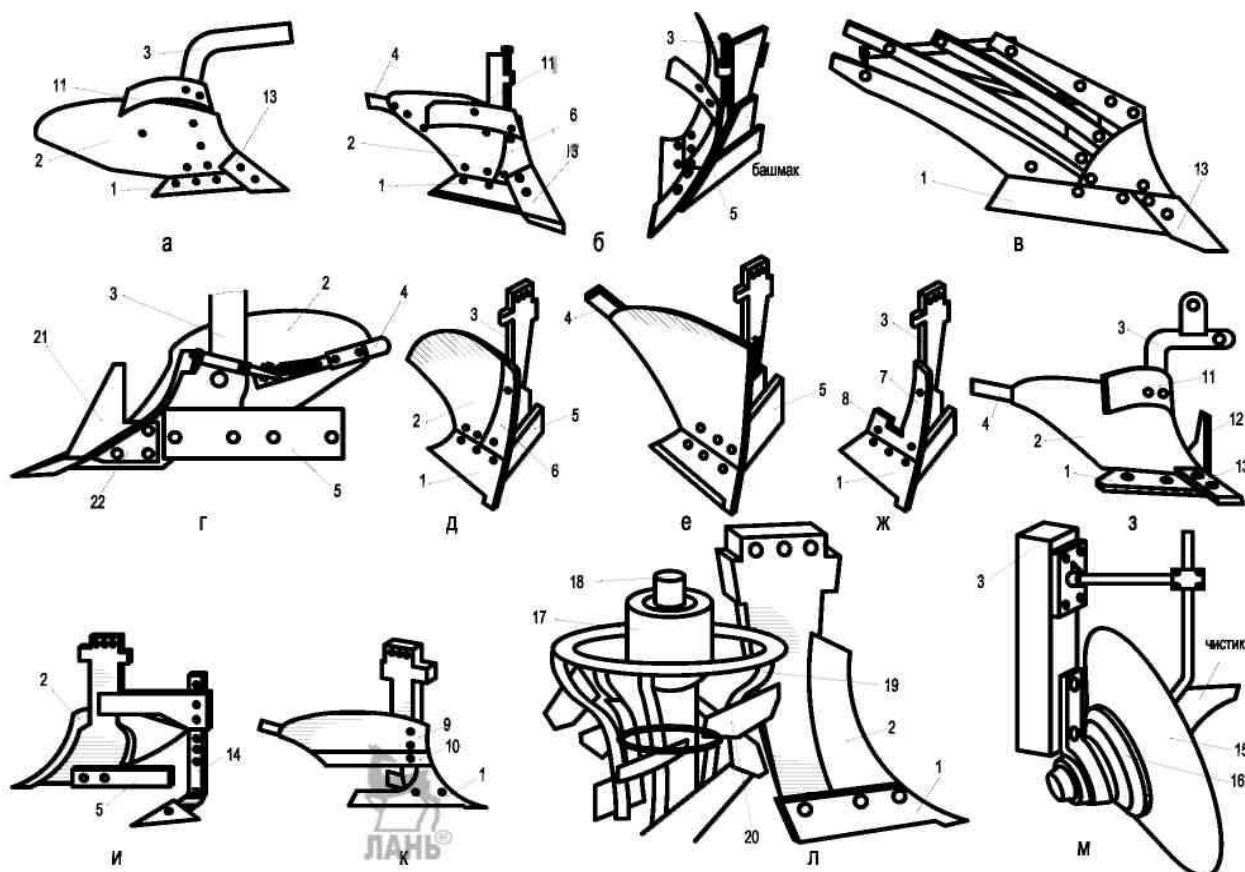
Типы корпусов плуга: а – корпус ПК-16.000; б – корпус ПЛП-01.000; в – полосовой корпус оборотного плуга LEMKEN; г – корпус плуга LEMKEN со сплошным отвалом; д – культурный; е – полувинтовой; ж – безотвальный; з – с накладным долотом; и – с почвоуглубителем; к – вырезной; л – комбинированный; м – дисковый; 1, 10 – лемехи; 2, 9 – отвалы; 3 – стойка; 4 – перо отвала; 5 – полевая доска; 6 – грудь отвала; 7 – щиток; 8 – уширитель; 11 – углосним; 12 – нож; 13 – долото; 14 – почвоуглубительная лапа; 15 – диск; 16 – шпиндель; 17 – корпус ротора; 18 – вал; 19 – ротор; 20 – лопатки; 21 – нож полевой доски; 22 – клин полевой доски
